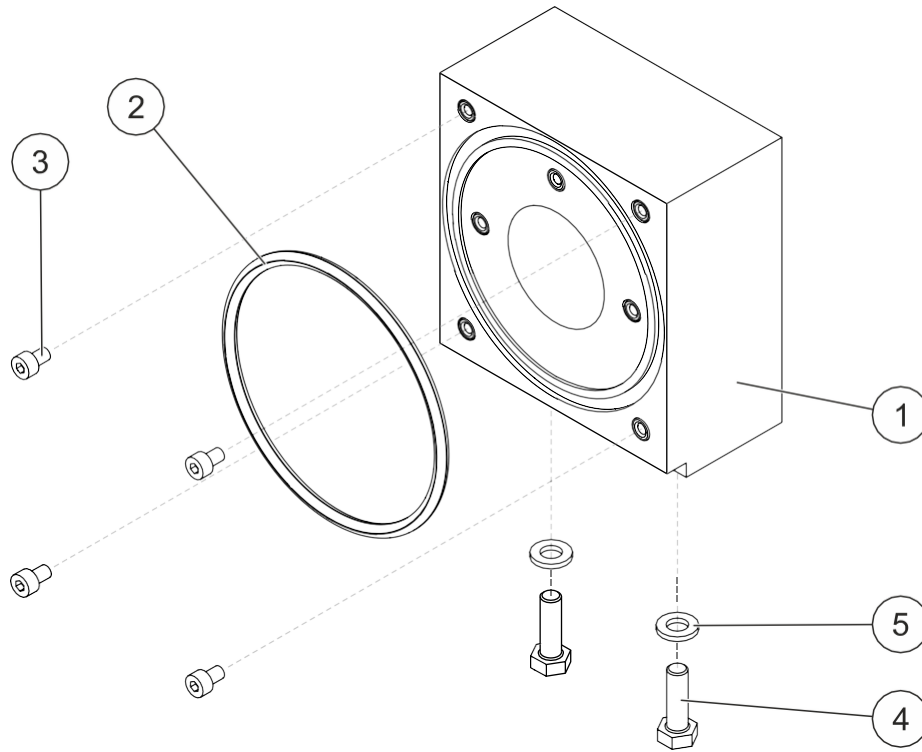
Baugruppe Motorflansch PQ15T-HT-NT
